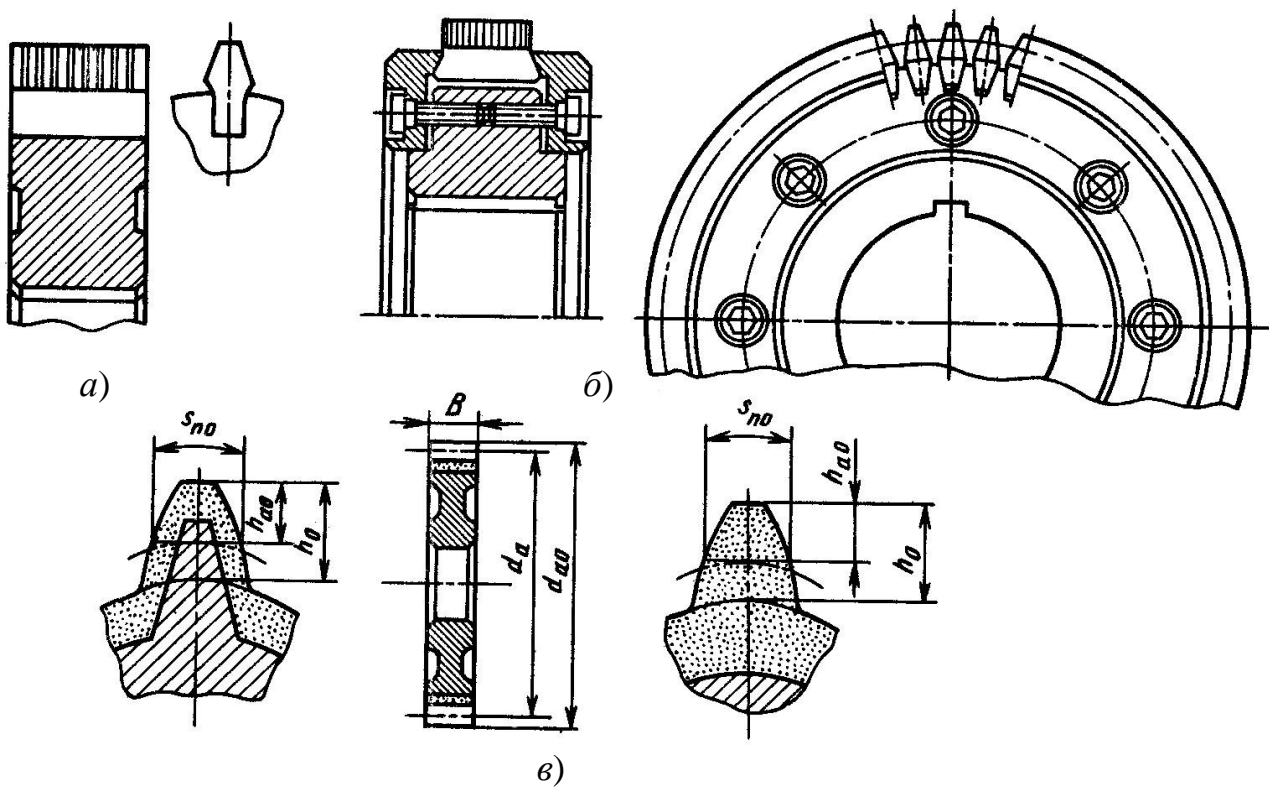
Шеверы твердосплавные (а и б) и алмазные (в)
